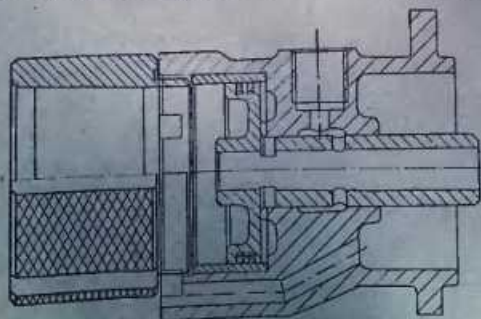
Конусная оправка для установки поршня в сборе с кольцами
